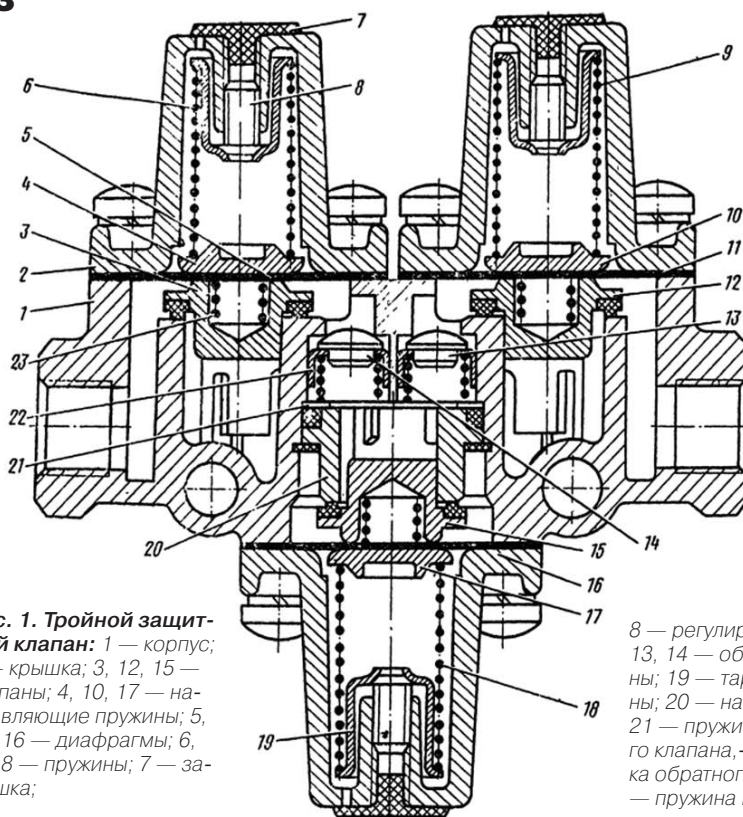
Тройной защитный клапан: 1 — корпус; 2 — крышка; 3, 12, 15 — клапаны; 4, 10, 17 — направляющие пружины; 5, 11, 16 — диафрагмы; 6, 9, 18 — пружины; 7 — заглушка;
